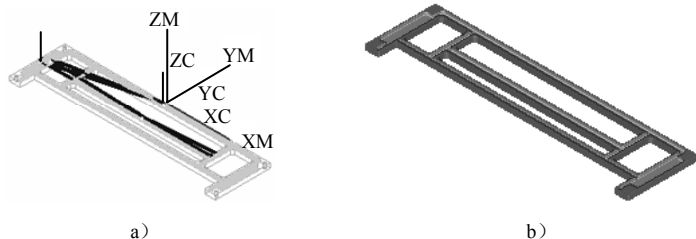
凹槽平面铣精加工的“刀具路径”和“实体切削验证”
